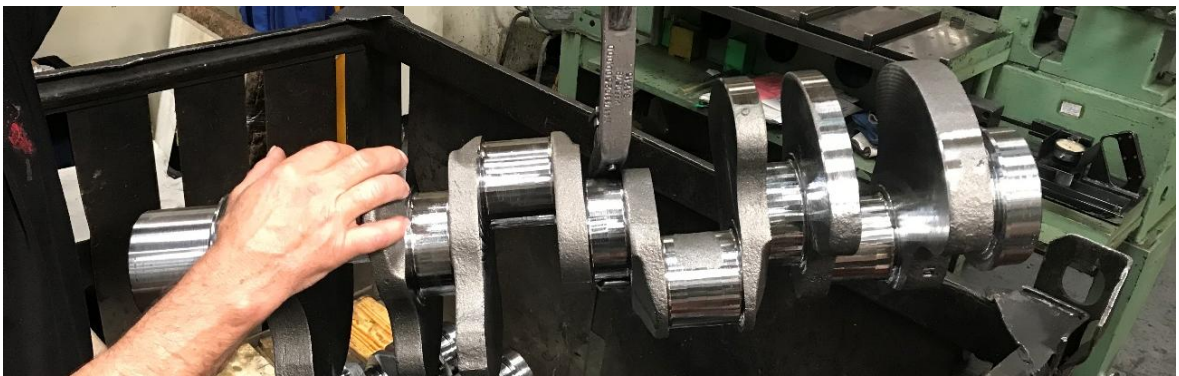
«Чернота» на обрабатываемых поверхностях вала 740.11-1005020
